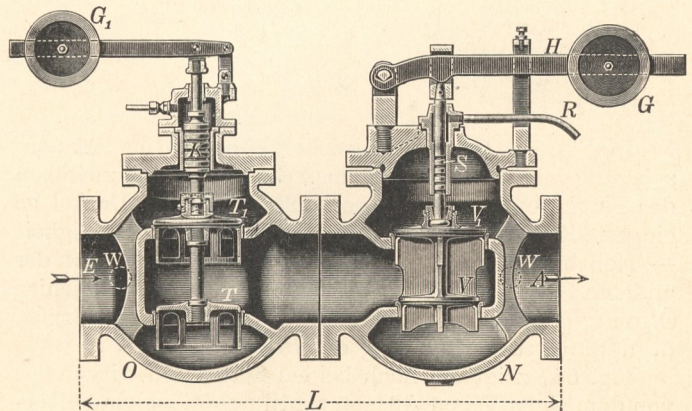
Verbund-Dampfdruckregler für Kesselgruppen mit verschiedener Spannung.
